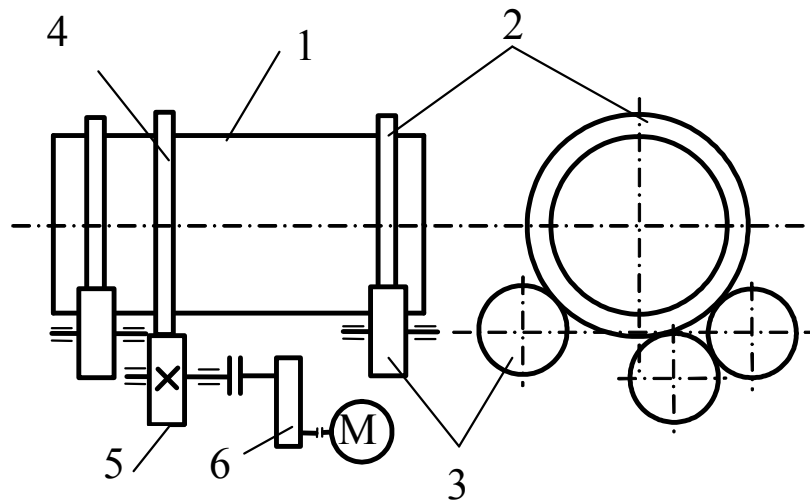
Кінематична схема барабана обертання з приводною шестернею
